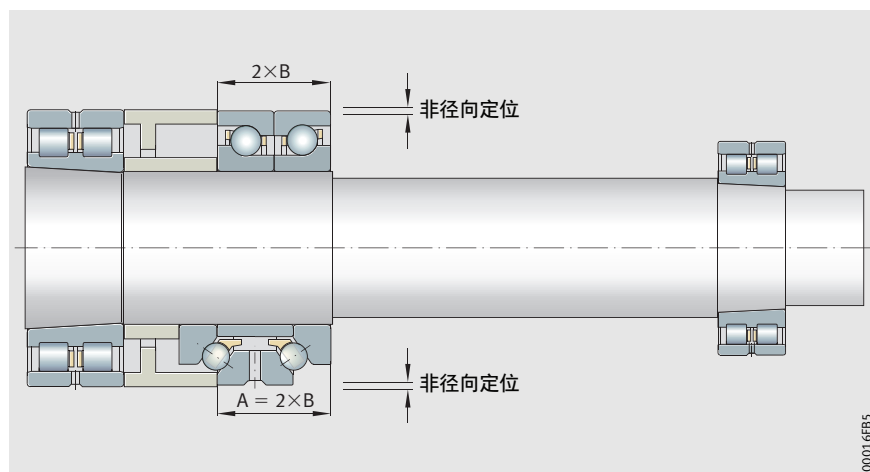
· 比较 – BAX 轴承与双向推力角接触球轴承
